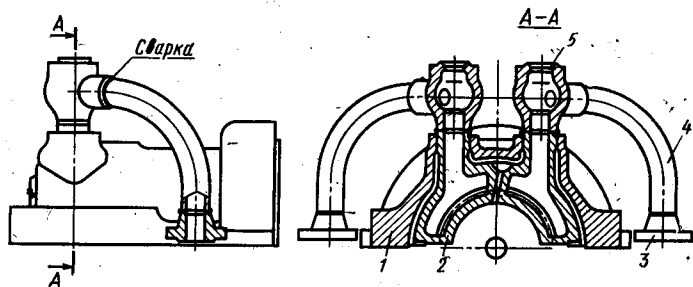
Верхняя половина сварно-литого корпуса с приваренными сопловыми и паровыми коробками:
